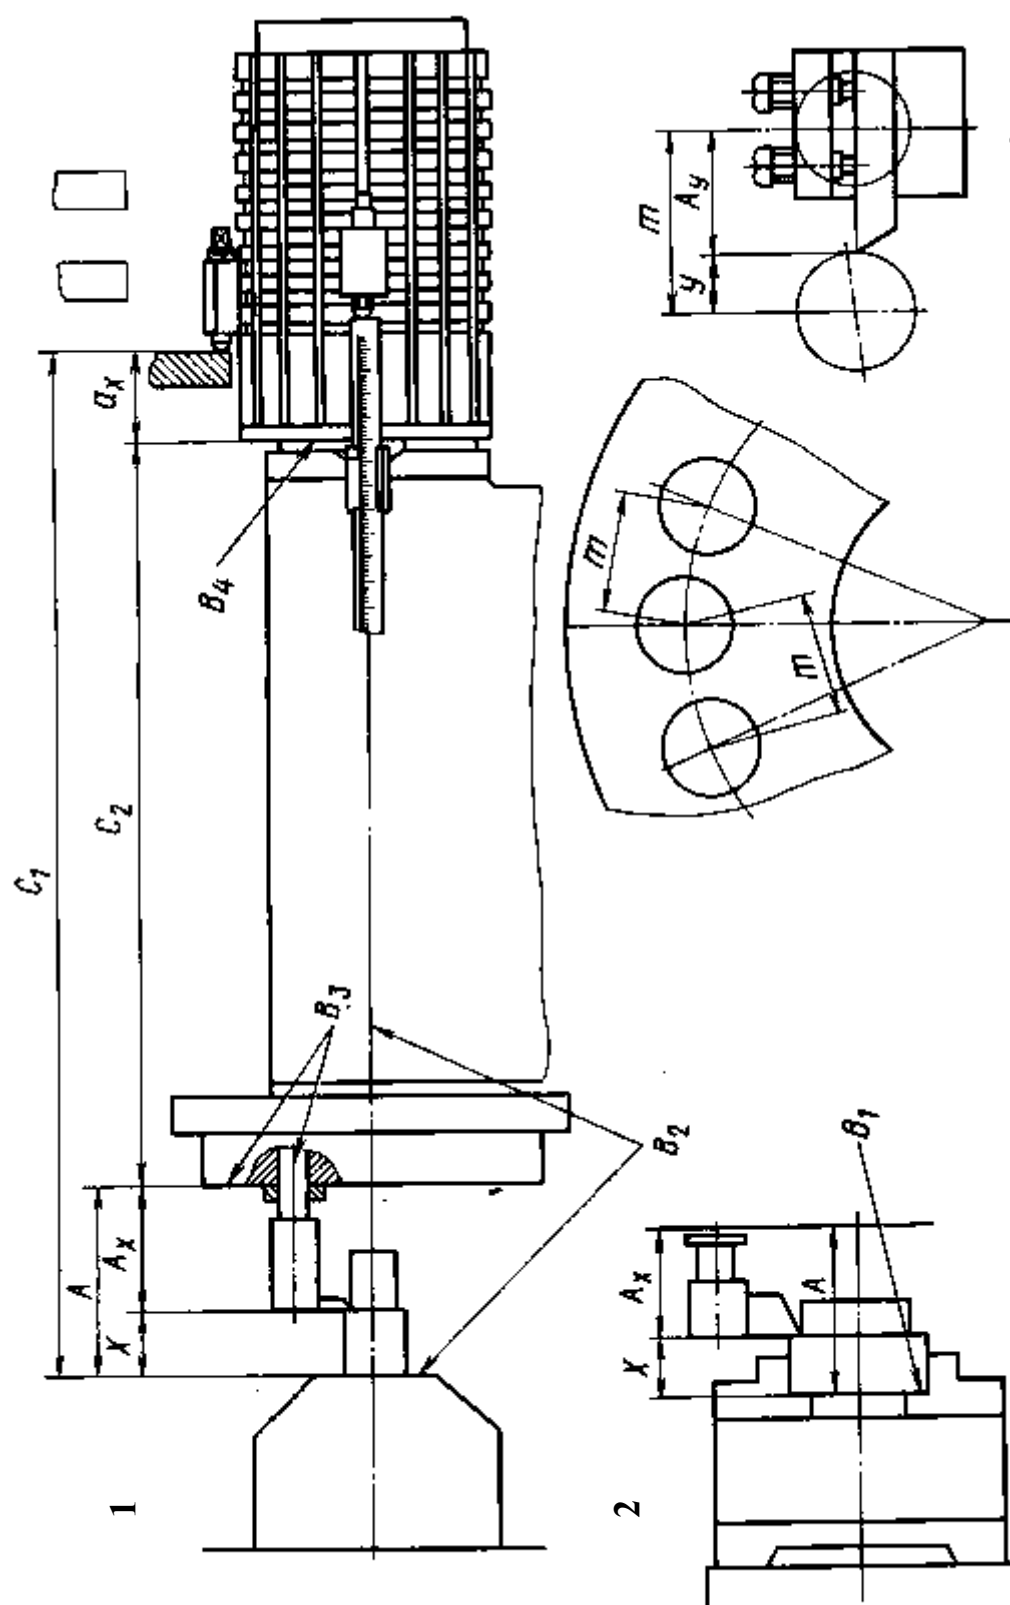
Схема наладки инструмента на станке: 1 – работа в цанговом патроне, 2 – работа в трехкулачковом патроне; B_1 – база детали; B_2 – основные отсчетные базы; B_3 – промежуточные отсчетные базы; B_4 – отсчетная база глубиномера
